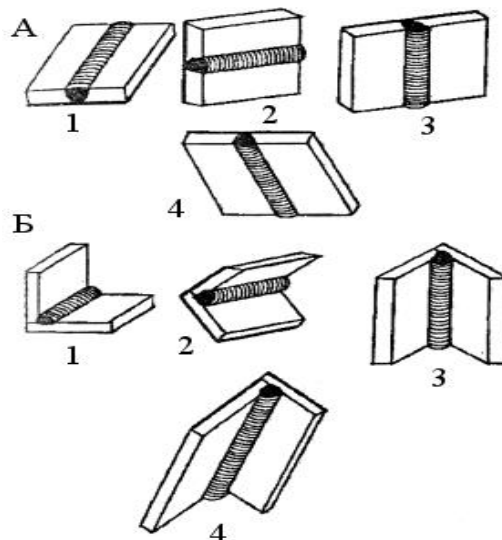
Основные положения сварных швов в пространстве: А – стыковые; Б – угловые; 1 – нижнее; 2 – горизонтальное; 3 – вертикальное; 4 – потолочное
